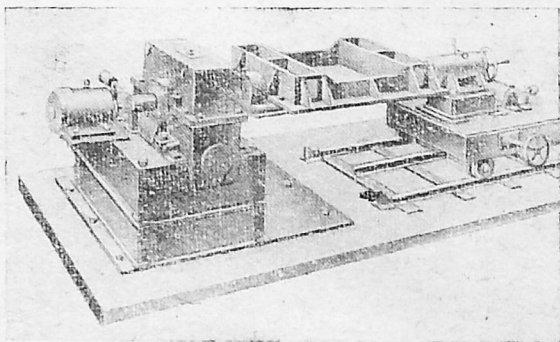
Двухстоечный кантователь для сварки узлов массой до 10 т.
